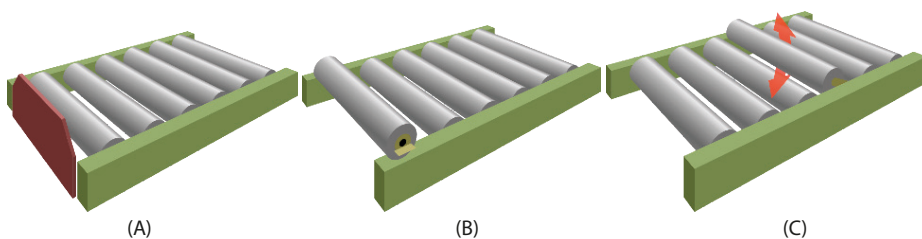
Dispositivos simples de parada de mercancías. (A) al final de la línea mediante una chapa soldada al bastidor; (B) al final de la línea mediante un rodillo pivotante que facilita la extracción manual de las mercancías; (C) en un punto intermedio de la línea mediante un rodillo pivotante. Extraído y adaptado de Lindkvist, R.G.T. (1985). *Handbook of Materials Handling*. Ellis Horwood Ltd. England.
